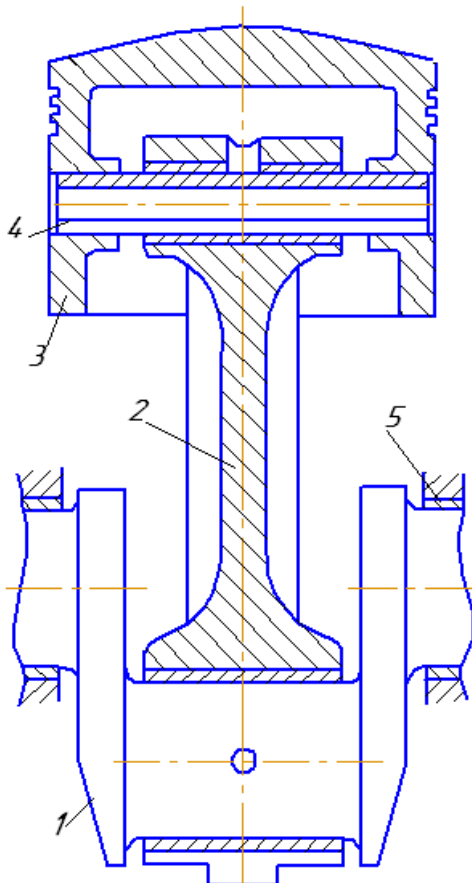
Кривошипно-поршневой узел двигателя
